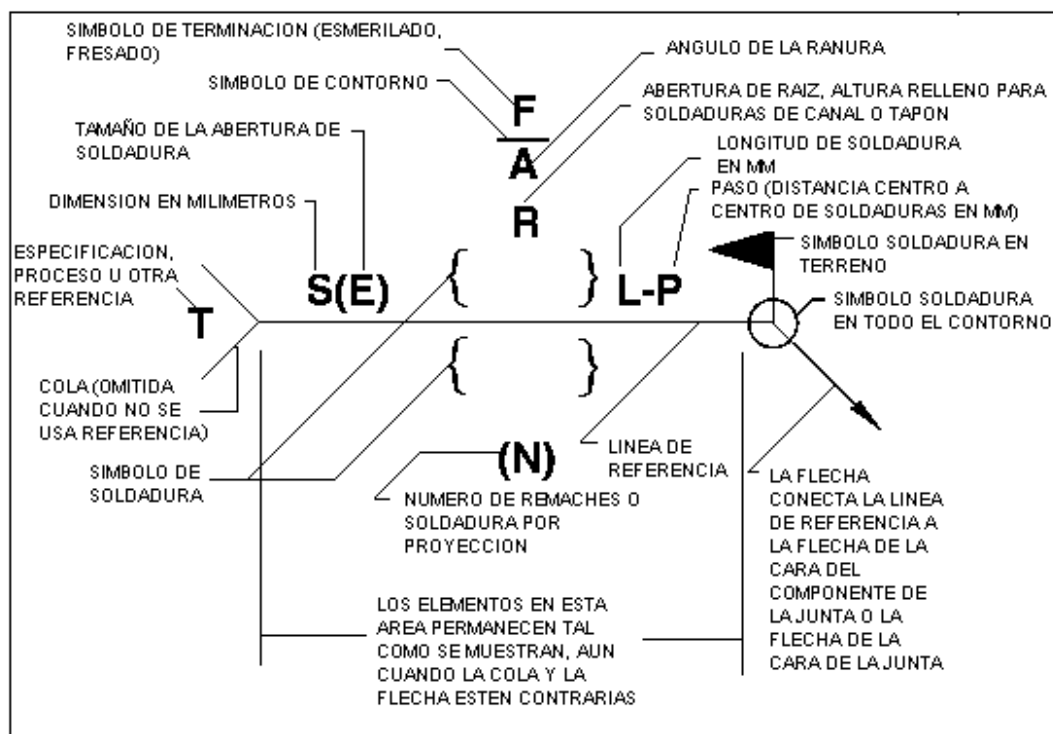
Ubicación estándar de los elementos de la simbología en soldadura.
